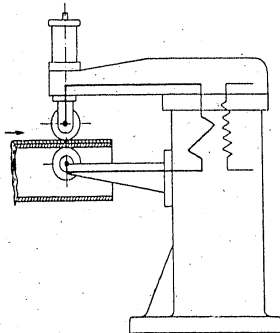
Elektrische Längsnahtschweißmaschine mit zwei Rollenelektroden (schematisch)
